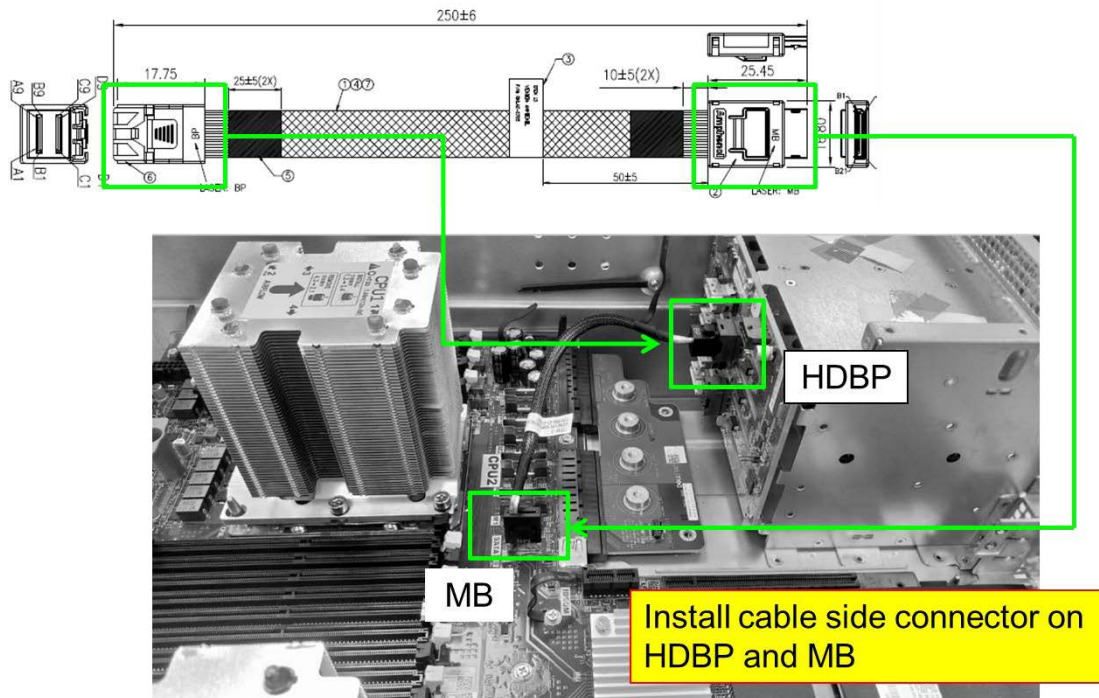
Assemblage du câble mini SAS HD, HDBP-MB
